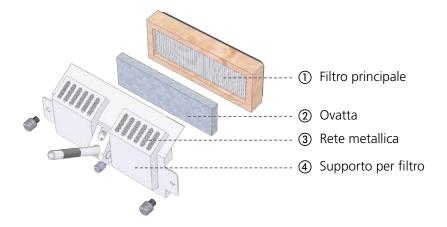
Filtro dell'aspiratore dei fumi di saldatura
